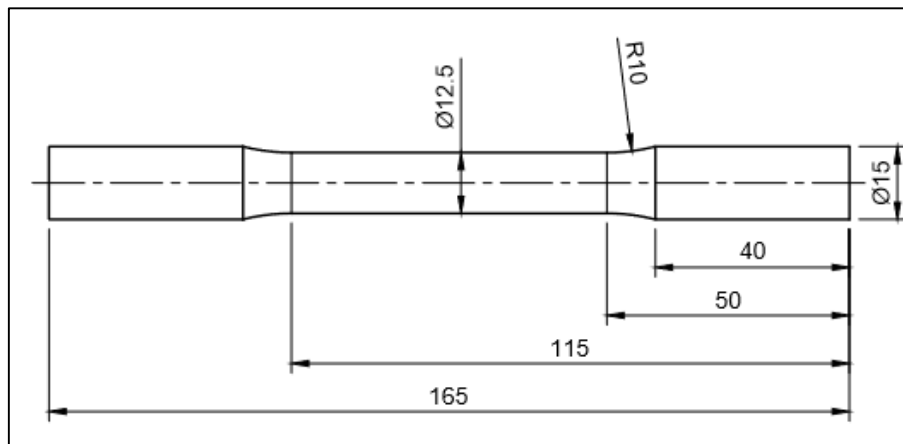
Diseño y dimensiones de la probeta según norma ASTM E8
